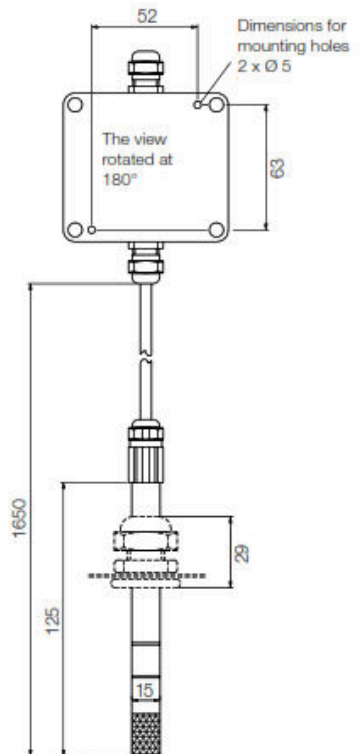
Вигляд та розміри KOBOLD AFK-G.
